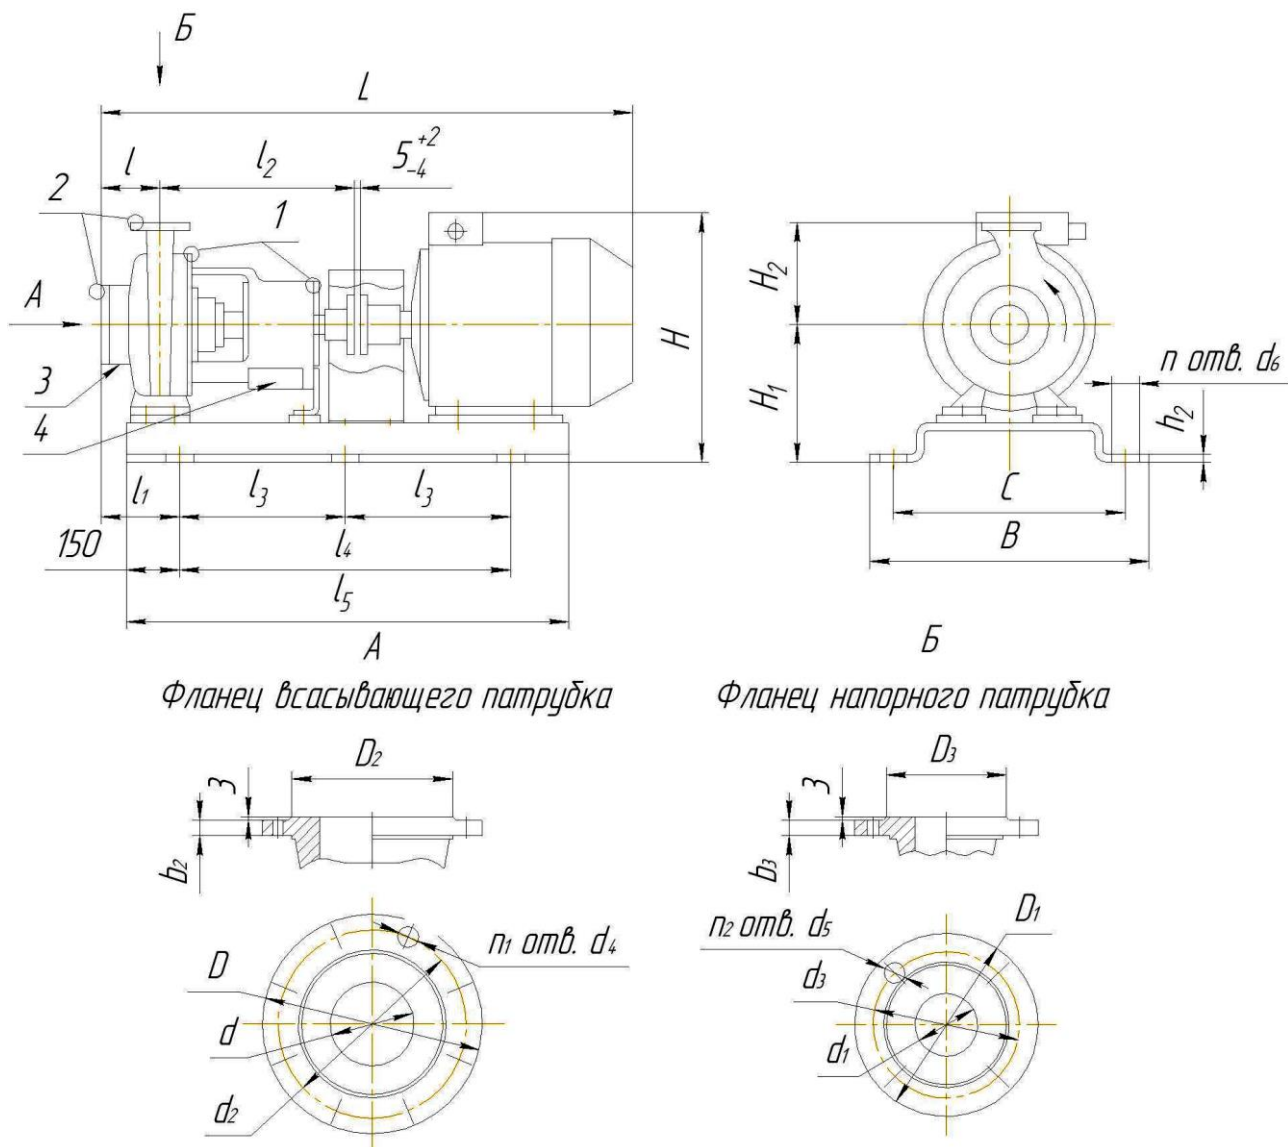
Габаритные и присоединительные размеры агрегатов типа «Х» в исполнении Д
